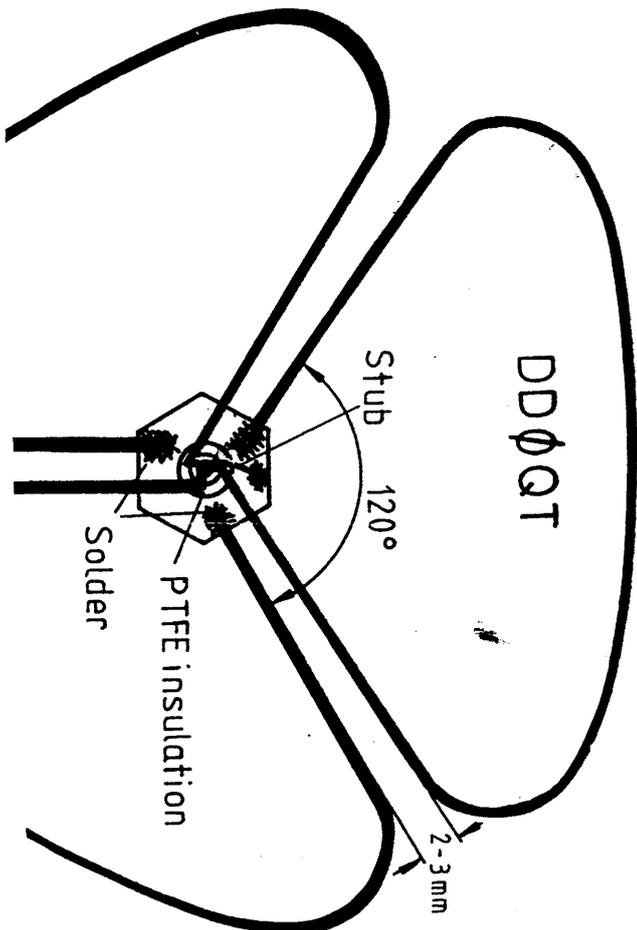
Antenne Big-Wheel pour la bande 23 cm vue de dessus. Chaque élément est à l'échelle 1. Les côtés Masse sont soudés sur la collerette; les côtés "chauds" sont soudés en place, sur le côté de l'âme du conducteur.
